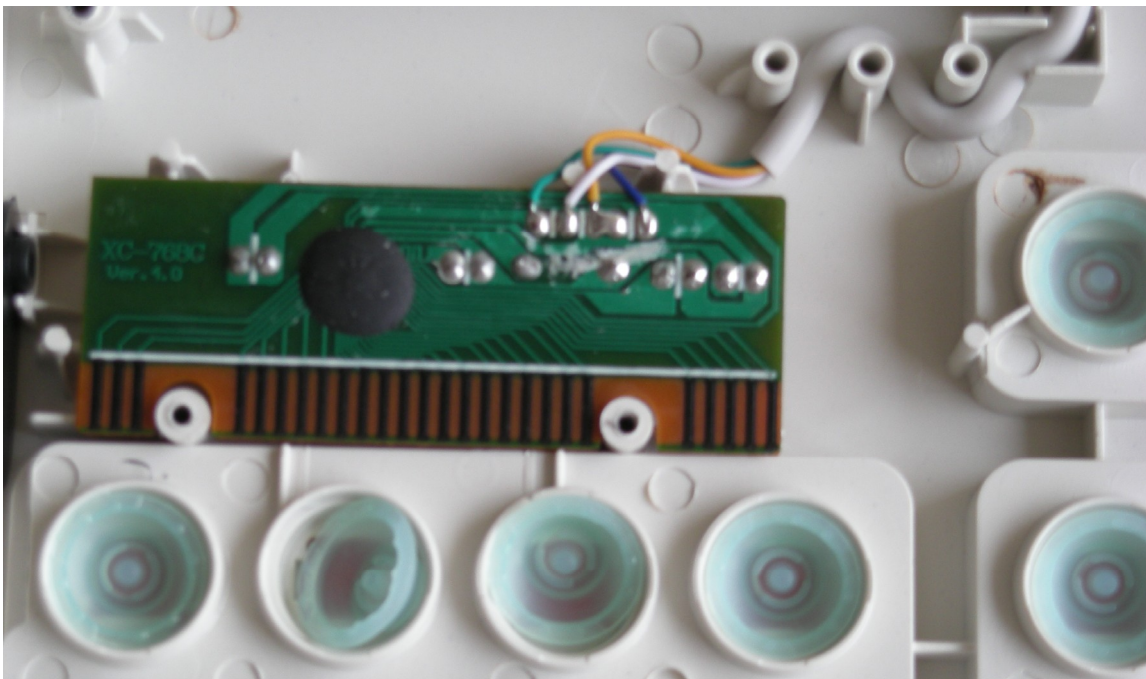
Foto do Teclado: vista detalhada do chip controlador
